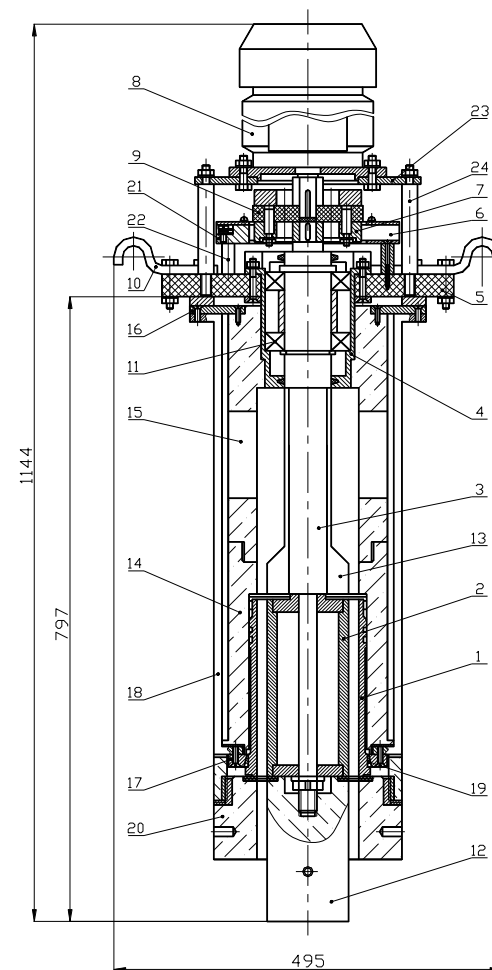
Промышленная установка: 1. цилиндр; 2. анод; 3. вал; 4. корпус; 5. несущая траверса; 6. графитовая щетка; 7. коллектор; 8. электродвигатель; 9. муфта; 10. токоподвод; 11. подшипник; 12. цилиндрическая гайка; 13. трубка; 14. обойма; 15. окна; 16. верхний кольцевой токоподвод; 17. нижний кольцевой токоподвод; 18. латунная штанга; 19. медная цанга; 20. кольцевая гайка; 21. щеткодержатель; 22. текстолитовая ножка; 23. металлическая плита; 24. стойка.
